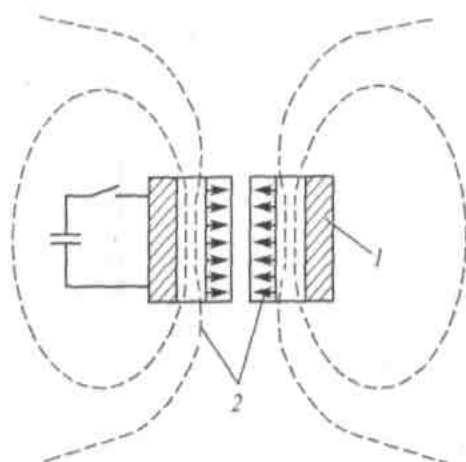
Схема магнитоимпульсной обработки: 1- индуктор; 2- заготовка; ---- магнитные линии; → - механические силы
